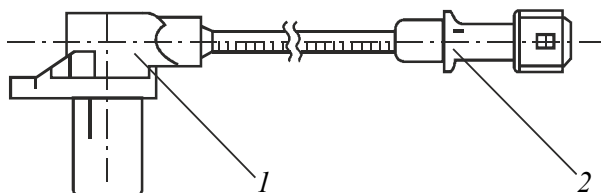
Соединительный кабель с трехконтактной вилкой:
